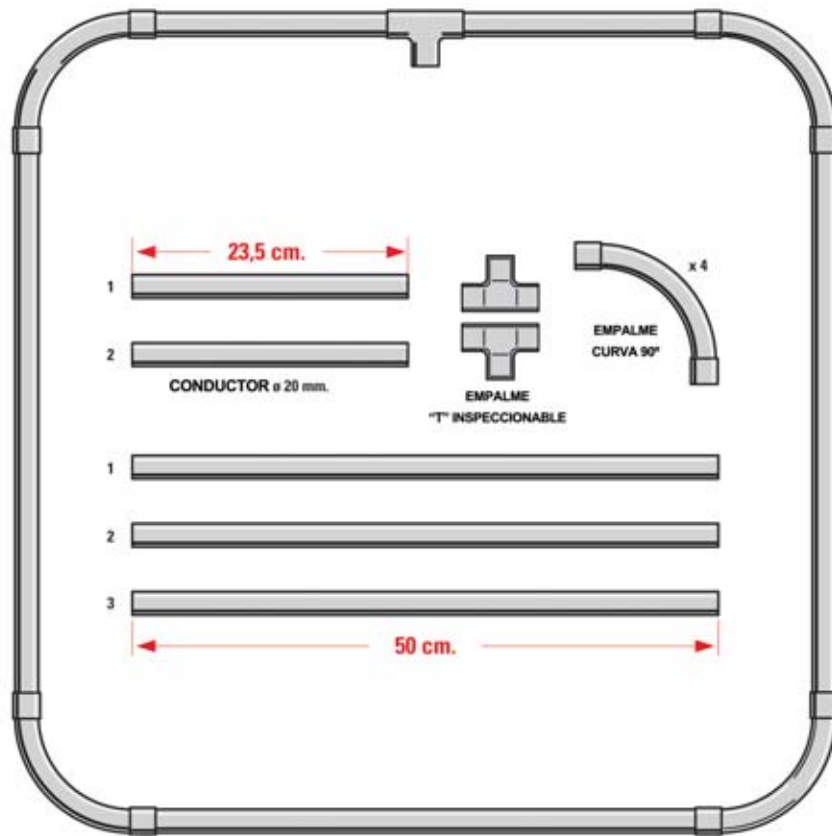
En este dibujo se indican las dimensiones de los componentes utilizados para la realización de nuestro prototipo de bobina captadora de forma cuadrada.
